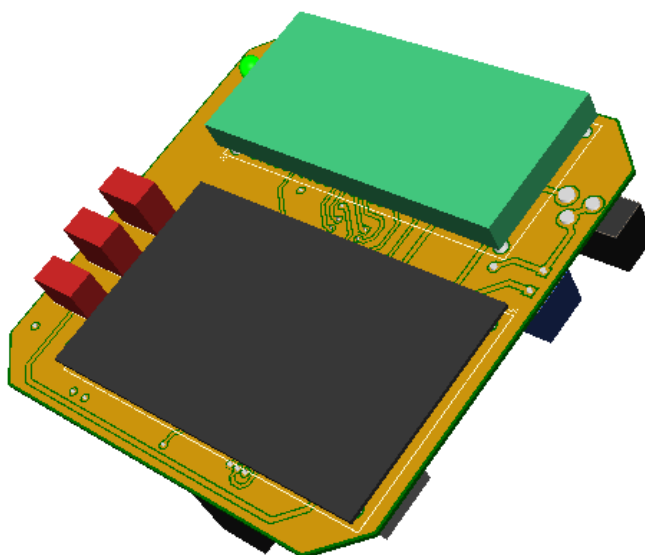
Capa inferior del PCB sin plano de tierra (GND)
